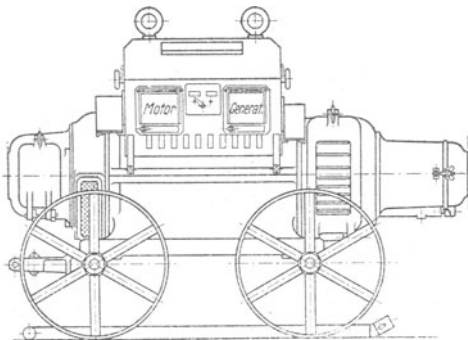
Äußeres Bild eines Gleichstrom-Schweißumformers.
